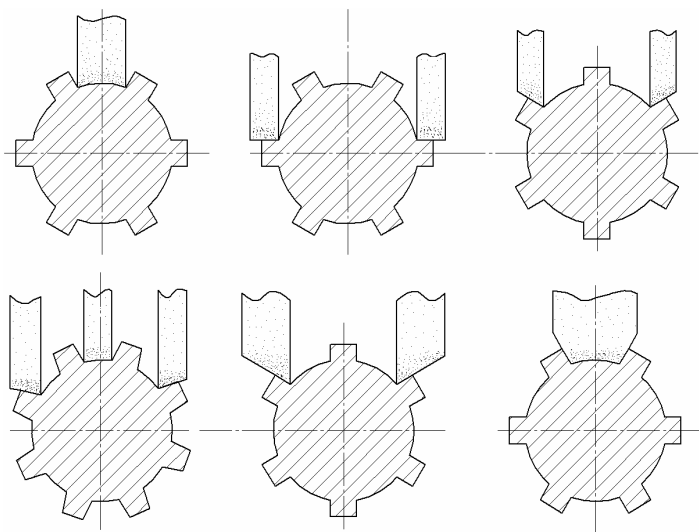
Схемы шлифования на шлицешлифовальных станках
